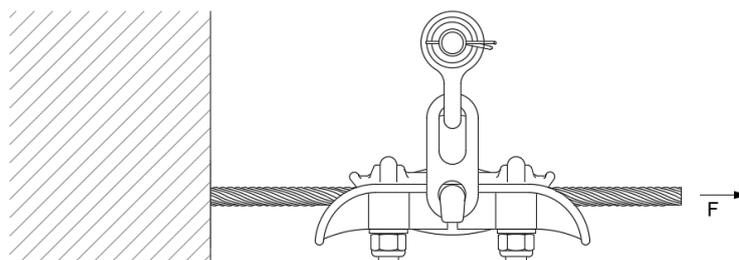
A – Montagem de pinça de suspensão para o ensaio de deslizamento.
